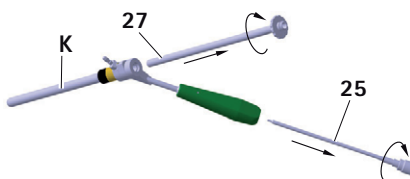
Demontage Führungshülse Ø 3,5 mm/4,0 mm
